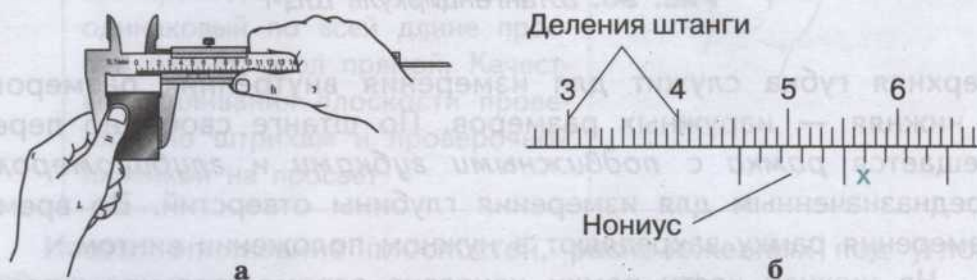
Отсчёт размера измеряемой детали по шкалам штангенциркуля
